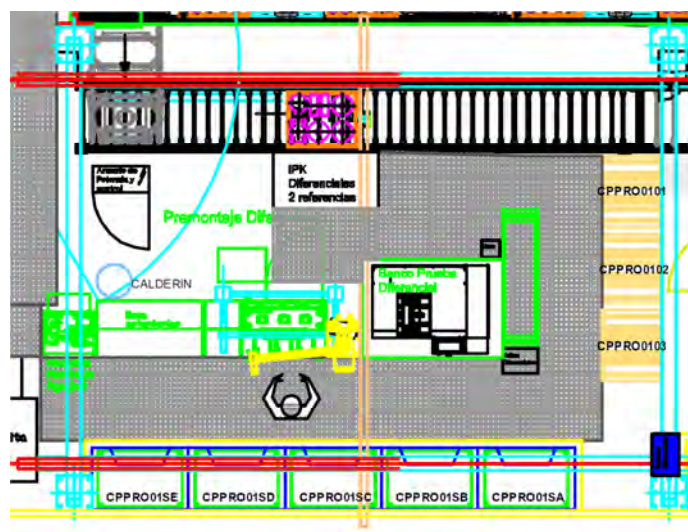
B LAYOUT PREMONTAJE DIFERENCIAL
